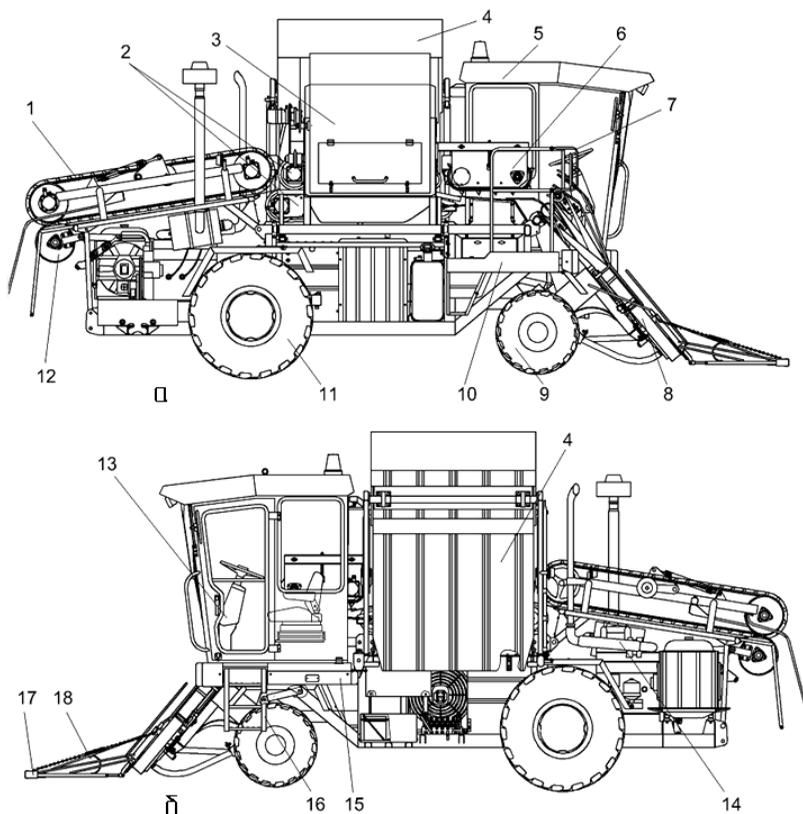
Комбайн льноуборочный самоходный КЛС-3,5:
